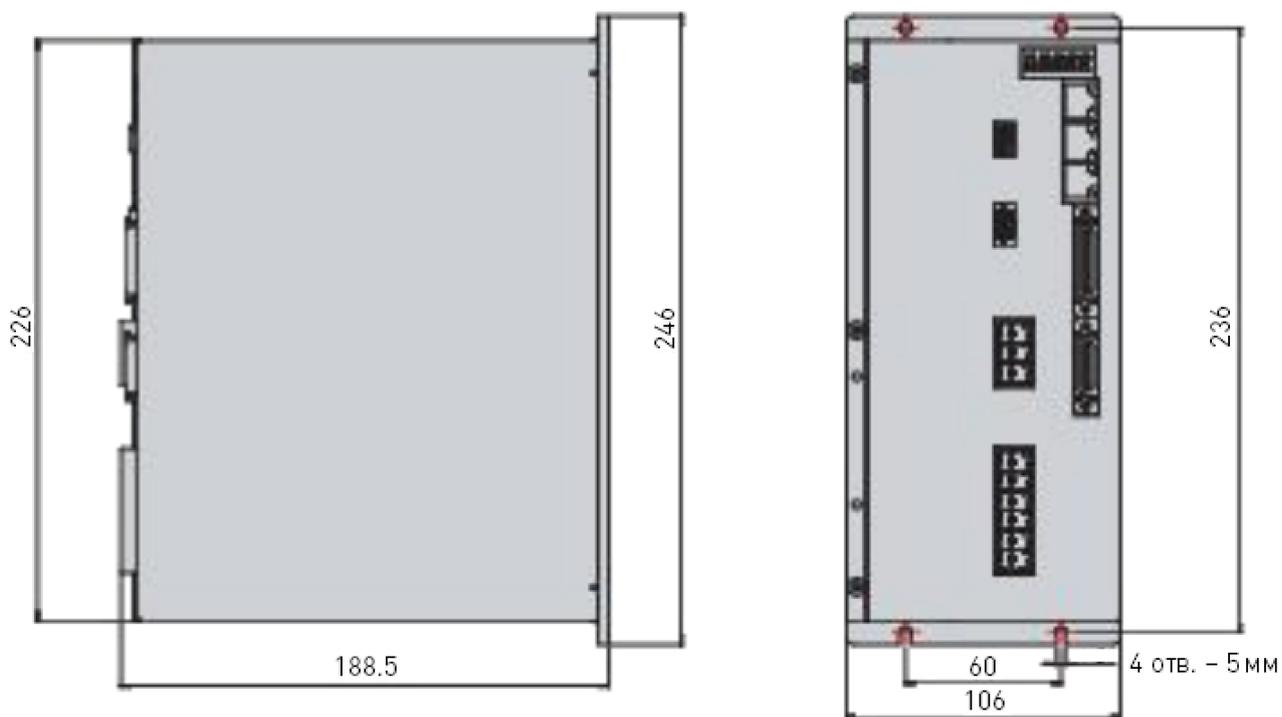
Габаритный чертеж драйверов ETD-A3012.
